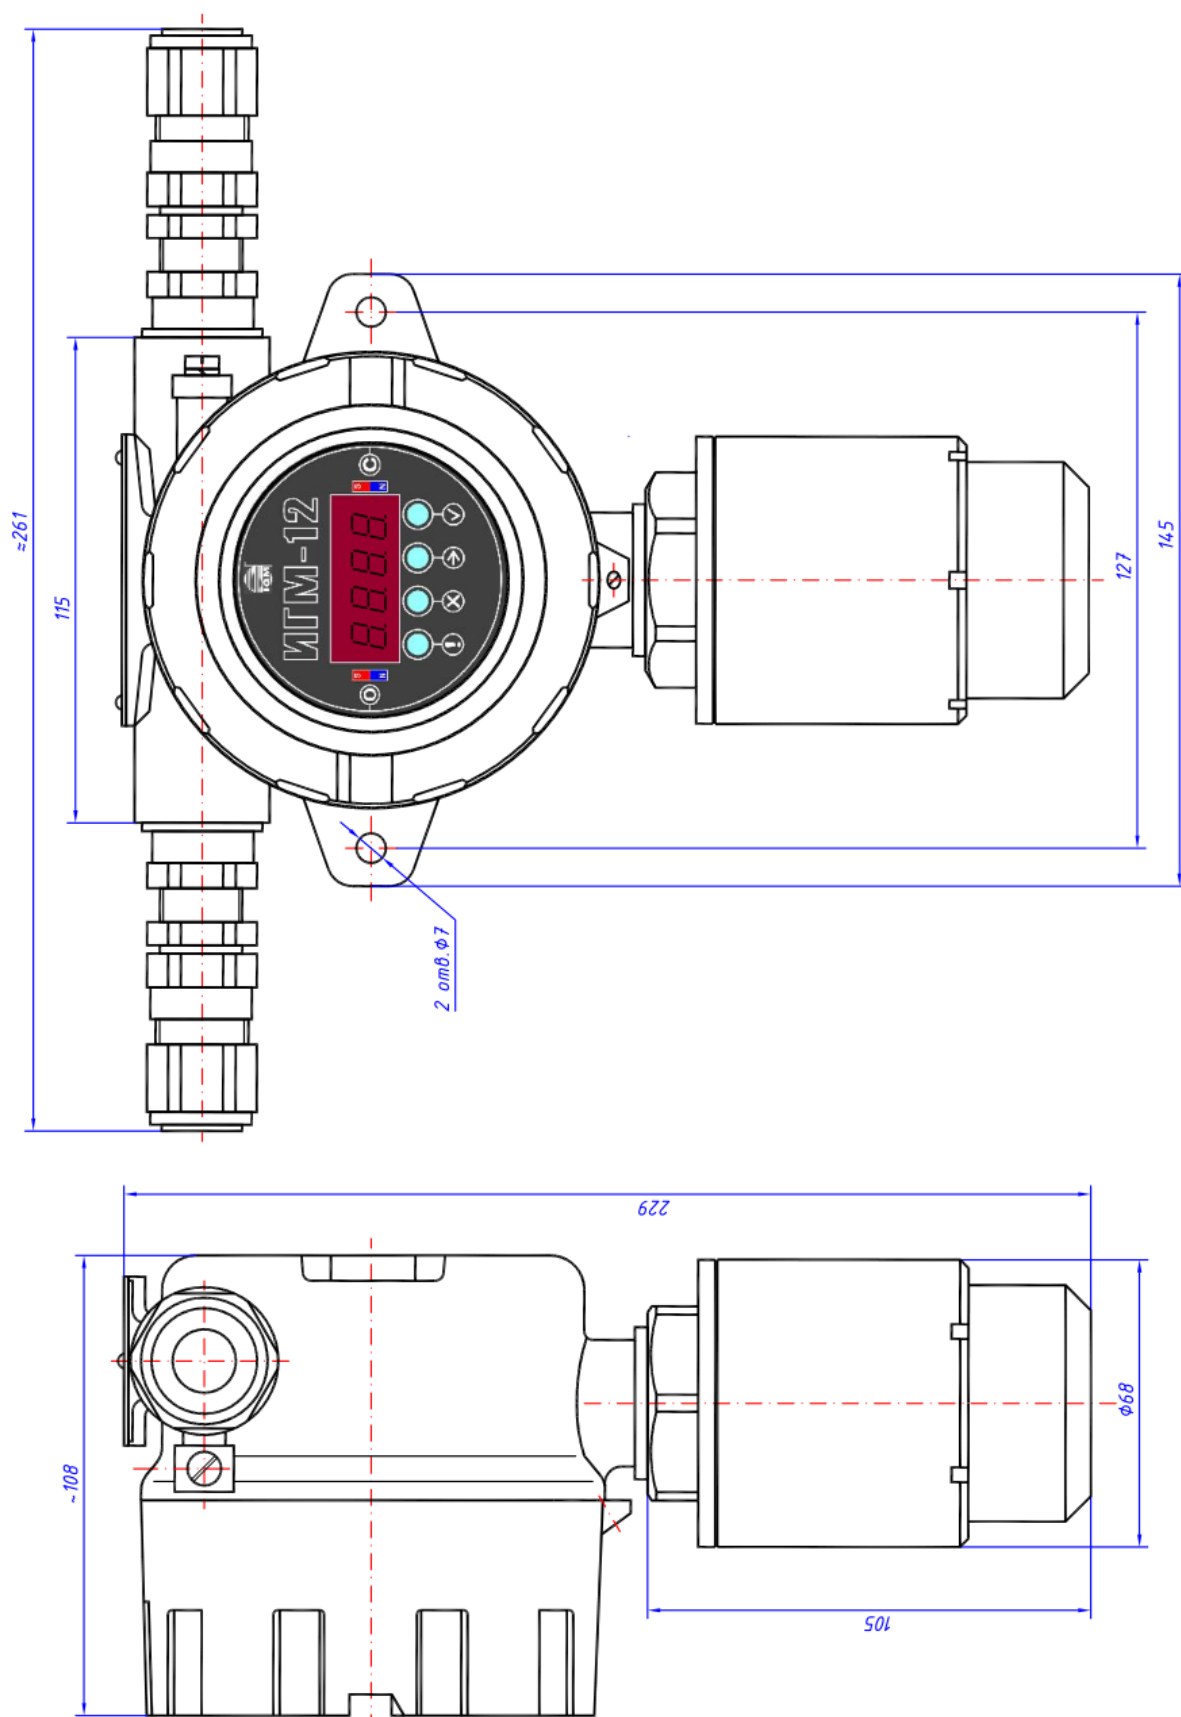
Габаритный чертеж ИГМ-12.
